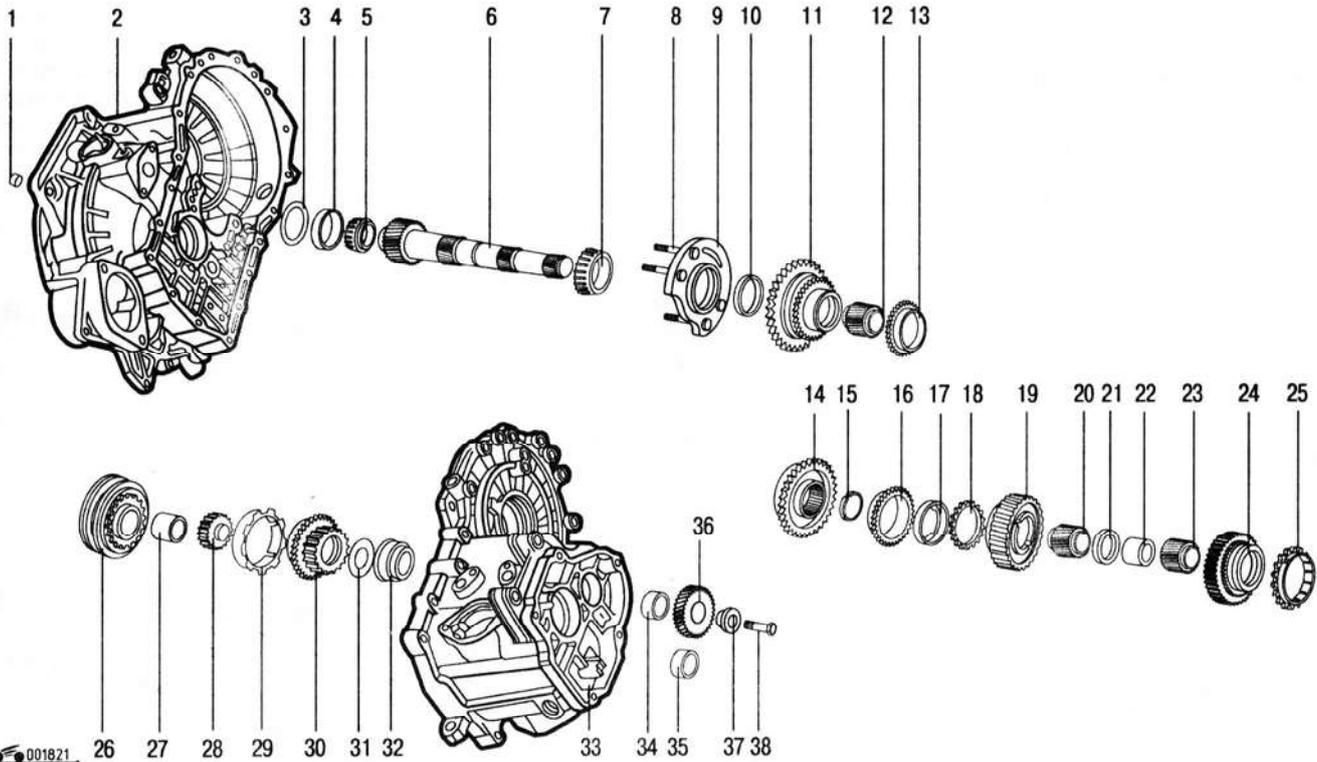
Вторичный вал и его детали: 1 — гайка; 2 — картер сцепления; 3 — шайба; 4 — чашка конического подшипника; 5 — конический подшипник (малый); 6 — вторичный вал; 7 — конический подшипник (большой); 8, 36 — болты; 9 — опора подшипника; 10, 21, 31 — упорные шайбы; 11 — шестерня I передачи; 12 — игольчатый подшипник шестерни I передачи; 13 — кольцо синхронизатора I передачи; 14 — ступица синхронизатора I и II передач; 15 — стопорное кольцо; 16 — кольцо синхронизатора II передачи; 17 — внешнее кольцо; 18 — внутреннее кольцо синхронизатора; 19 — шестерня II передачи; 20 — игольчатый подшипник шестерни III передачи; 22 — втулка игольчатого подшипника; 23 — игольчатый подшипник шестерен III передачи; 24 — шестерня III передачи; 25 — кольцо синхронизатора III передачи; 26 — ступица синхронизатора III и IV передач; 27 — втулка игольчатого подшипника; 28 — игольчатый подшипник шестерни IV передачи; 29 — кольцо синхронизатора IV передачи; 30 — шестерня IV передачи; 32 — игольчатый подшипник; 33 — картер коробки передач; 34 — опорная втулка; 35, 37 — втулки; 36 — шестерня V передачи
